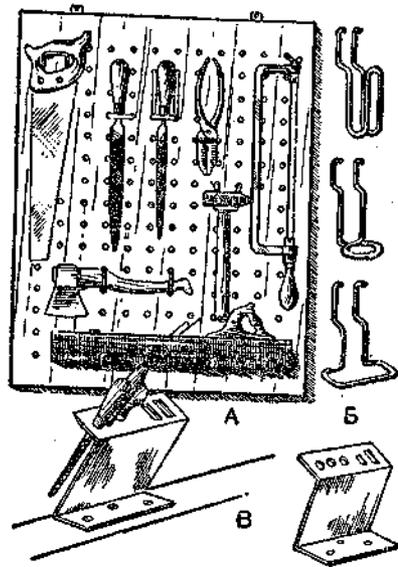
Хранение инструментов у рабочего стола: А — деревянный или фанерный щит с высверленными отверстиями; Б — проволочные вставки для крепления инструментов на щите; В — подставка из жести для хранения инструментов.
